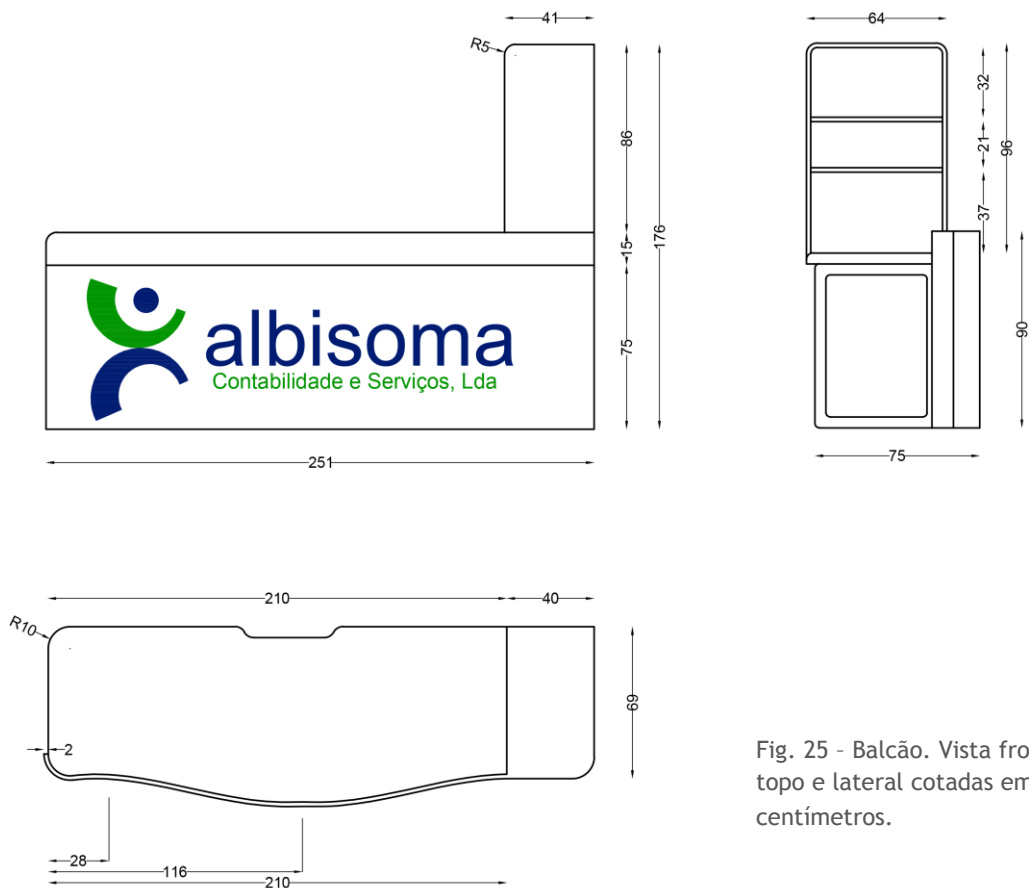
Balcão. Vista frontal, topo e lateral cotadas em centímetros.
